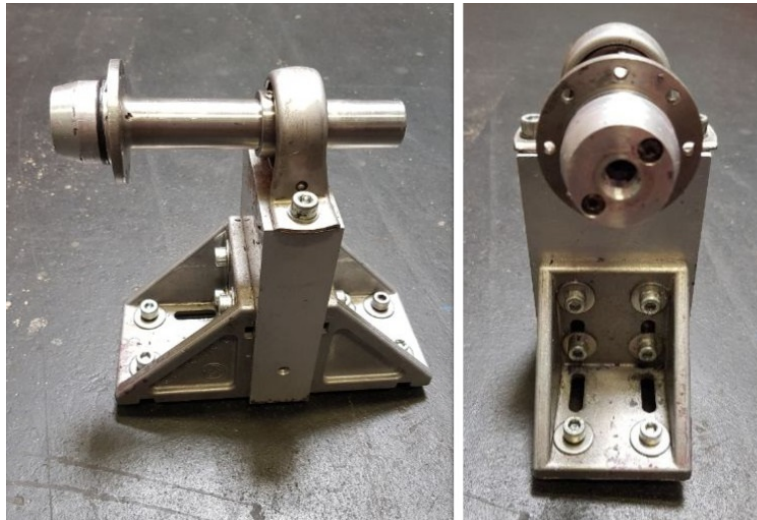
Aluminiumplatte mit Kugel-Stehlager mit Blechgehäuse aus Edelstahl und Flanschswelle
